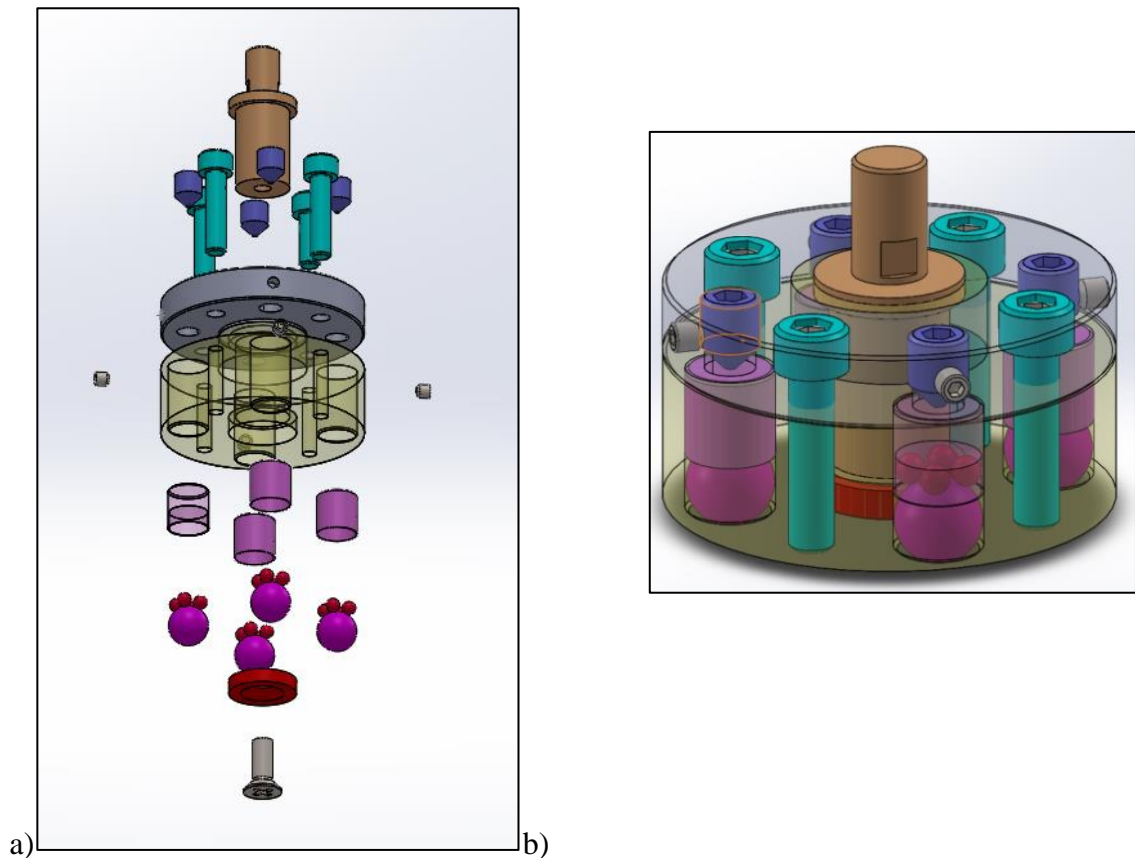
Têtes multi-billes a) vue du montage b) vue éclatée
